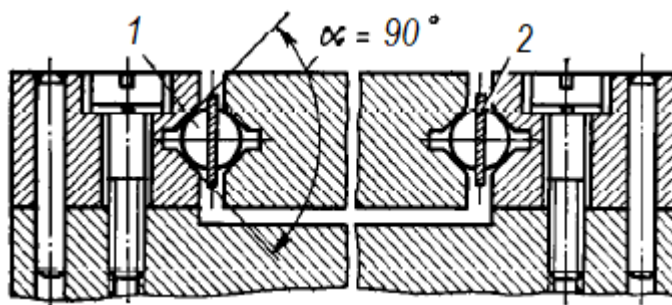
Типовая конструктивная схема шариковой направляющей
